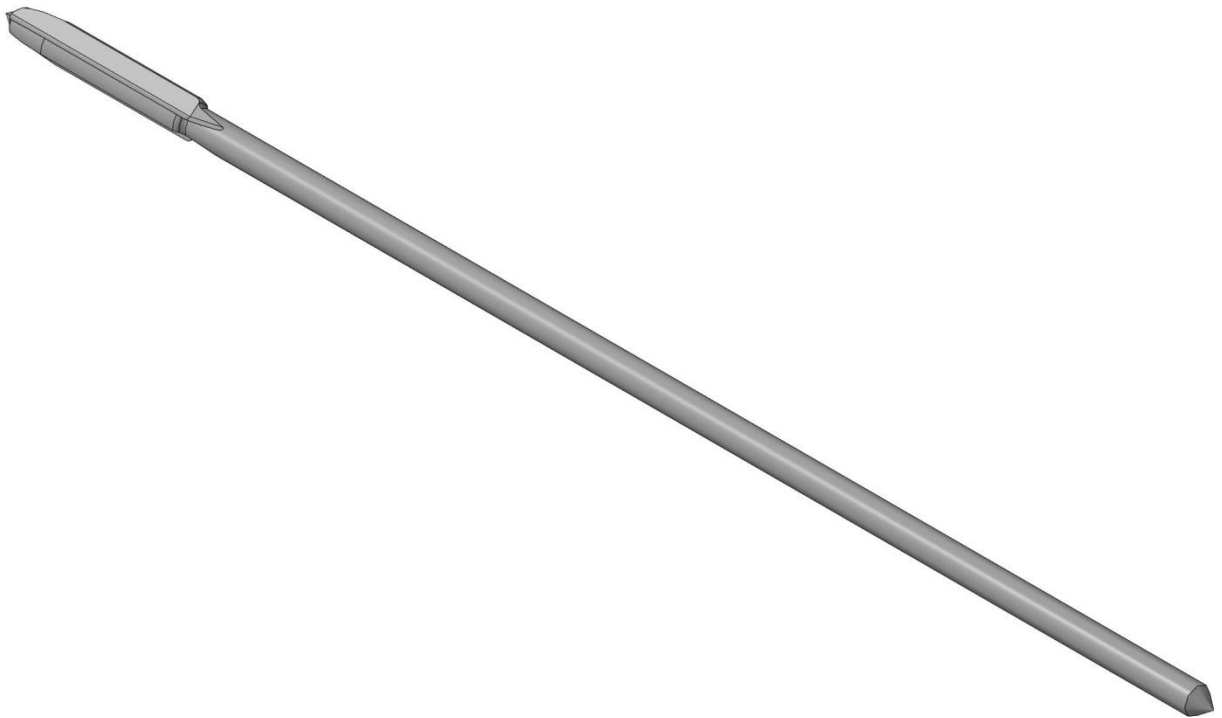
Тривимірна модель заготовки мітчика
